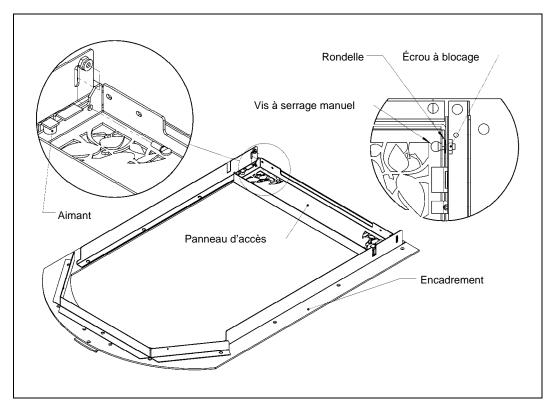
Installation et retrait du panneau d'accès inférieur.
